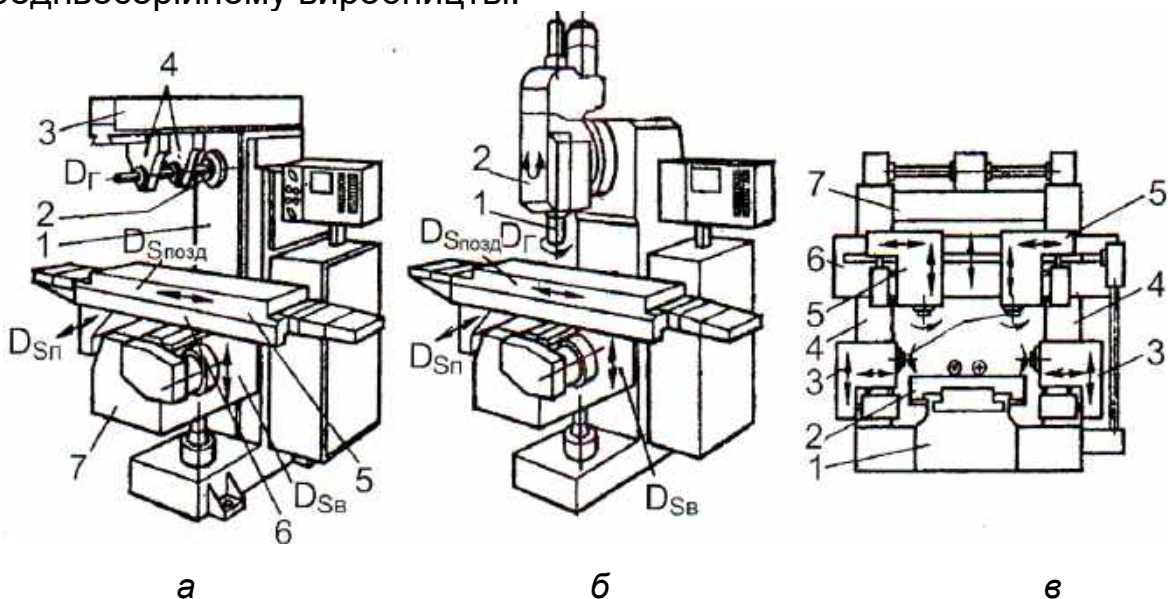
Основні види фрезерних верстатів: а – горизонтальний (1 – станина; 2 – шпindel; 3 – хобот; 4 – підвіска; 5 – стіл; 6 – поперечний полозок; 7 – консоль); б – вертикальний (1 – шпindel; 2 – головка); в – поздовжньо-фрезерний (1 – шпindel; 2 – стіл; 3, 6 – шпиндельна бабка; 4 – стояки; 5 – траверса; 7 – портал)
